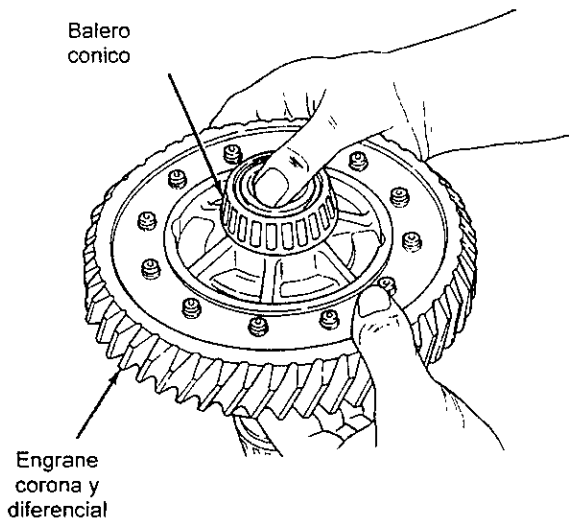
Ensamble de diferencial y engrane corona (Cortesía Chrysler)
